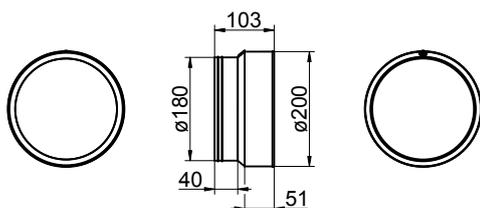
Dimensions de raccord de transition DN180 (dimensions en mm)
